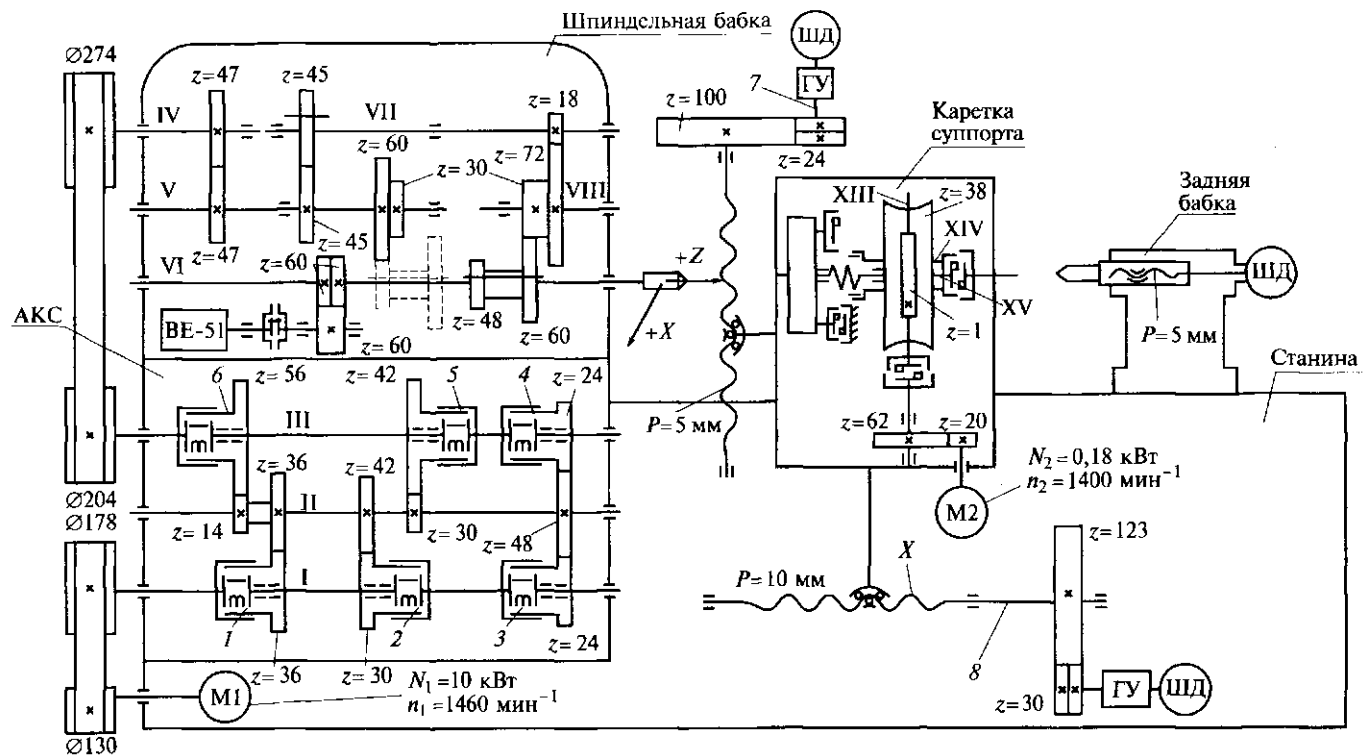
Кинематическая схема токарного патронно-центрового станка с контурной системой ЧПУ:
